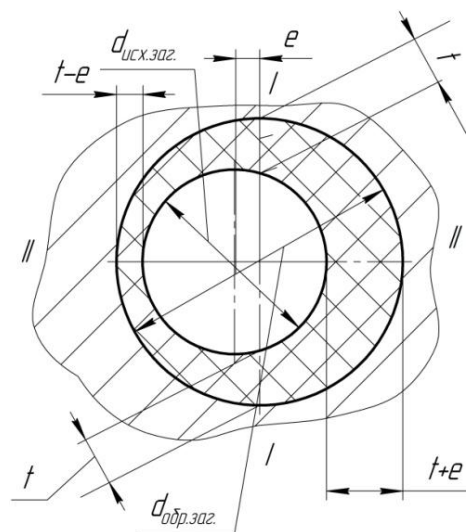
Схема образования неравномерности припуска от смещения оси заготовки.
